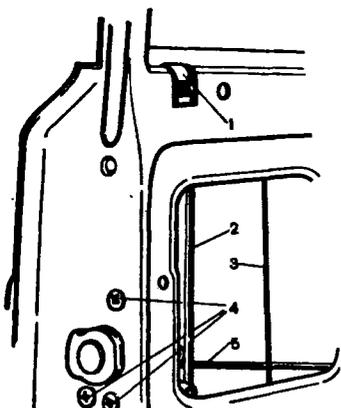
Крепление замка двери: 1 - кнопка блокировки замка; 2 - тяга кнопки блокировки; 3 - трос стеклоподъемника; 4 - винты крепления замка; 5 - тяга внутреннего привода замка
